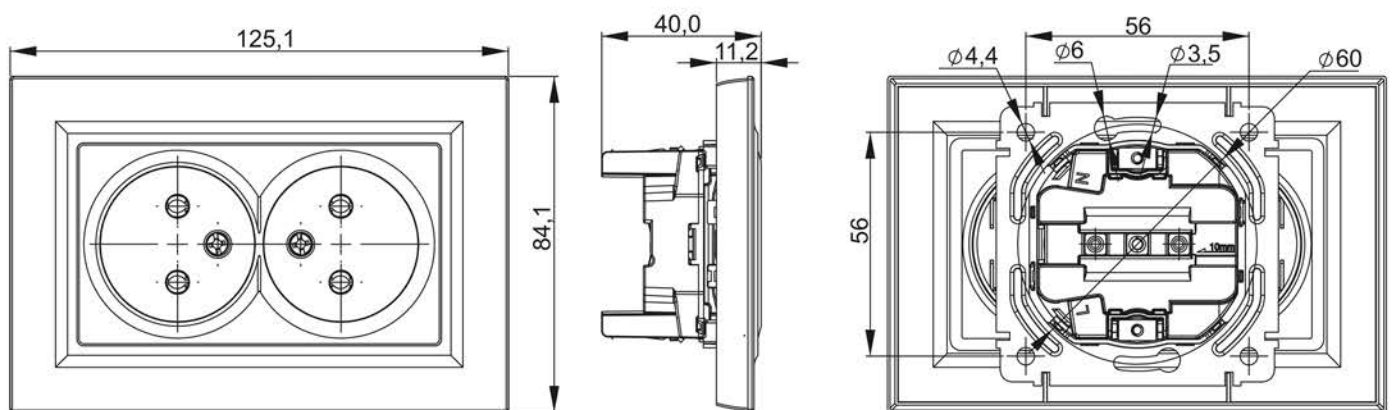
Габаритные и присоединительные размеры розеток (лист 1 из 5 / Figure 2 – Overall and mounting dimensions of sockets (sheet 1 of 5) / 2-сურет – Розетканың габаритті және қосылатын өлшемдері (5-ден 1-парақ) / Figura 2 – Dimensiunile generale și de instalare sunt (foaia 1 din 5) / Şəkil 2 – Rozetkaların ümumi və əlaqə ölçüləri (5-dən 1-ci vərəq) / Նկար 2 – Վարդակների ընդհանուր և միացման չափերը (թերթ 1 5-ից) / ნახატი 2 – როზეტების გაბარიტული და საყენებელი ზომები (ფურცელი 1 5-დან) / 2-сурет – Розеткалардын көлөм жана туташтырылуучу өлчөмдөрү (барак 1 ичинен 5) / Расми 2 – Андозаи умумӣ ва пайвасткуандаи васлак (варақаи 1 аз 5) / 2-rasm – Rozetkalarining gabaritlari bo'yicha hamda o'rnatilishdagi o'lchamlari (5 varaqdan 1-varaq)
